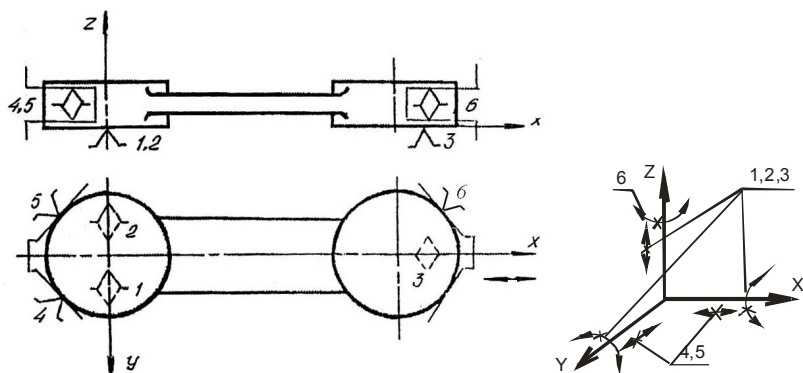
Теоретическая схема базирования заготовки по плоскости и двум наружным цилиндрическим поверхностям
